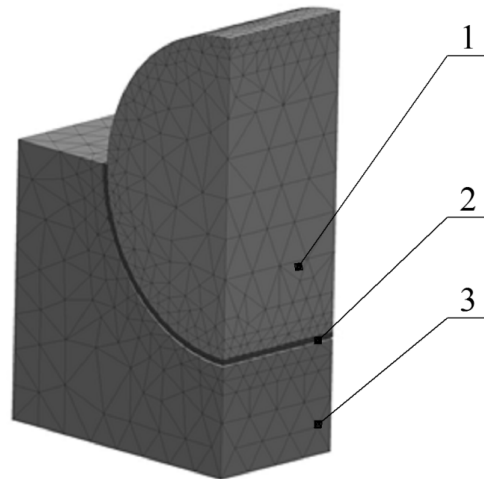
Розрахункова твердотільна модель підшипникового вузла із сіткою кінцевих елементів: 1 – вал; 2 – підшипник; 3 – корпус рамового підшипника
